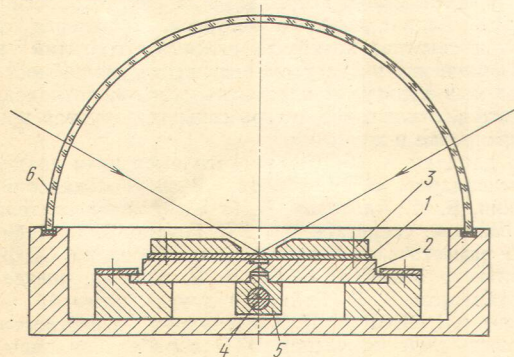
Схема вакуумной камеры для сварки плоских образцов
